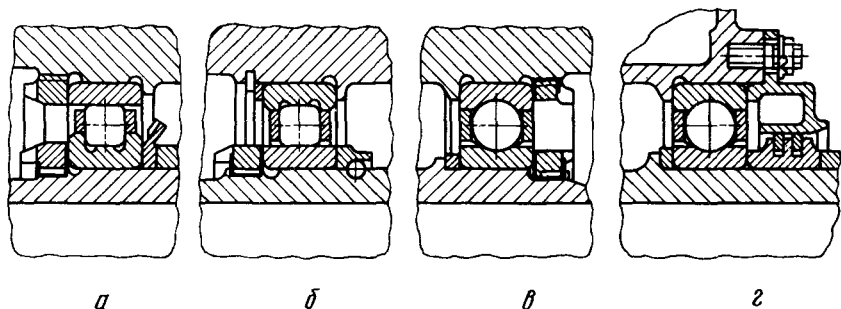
Примеры закрепления роликовых (а, б) и шариковых (в, г) подшипников на валу и в корпусе
